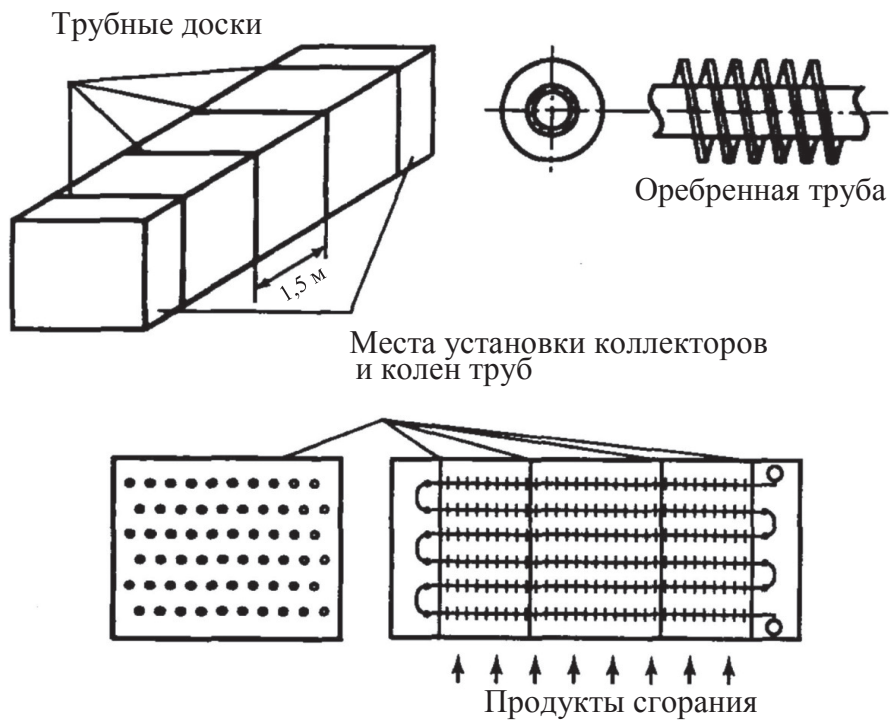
Компоновка блока оребренных поверхностей нагрева вертикального КУ
